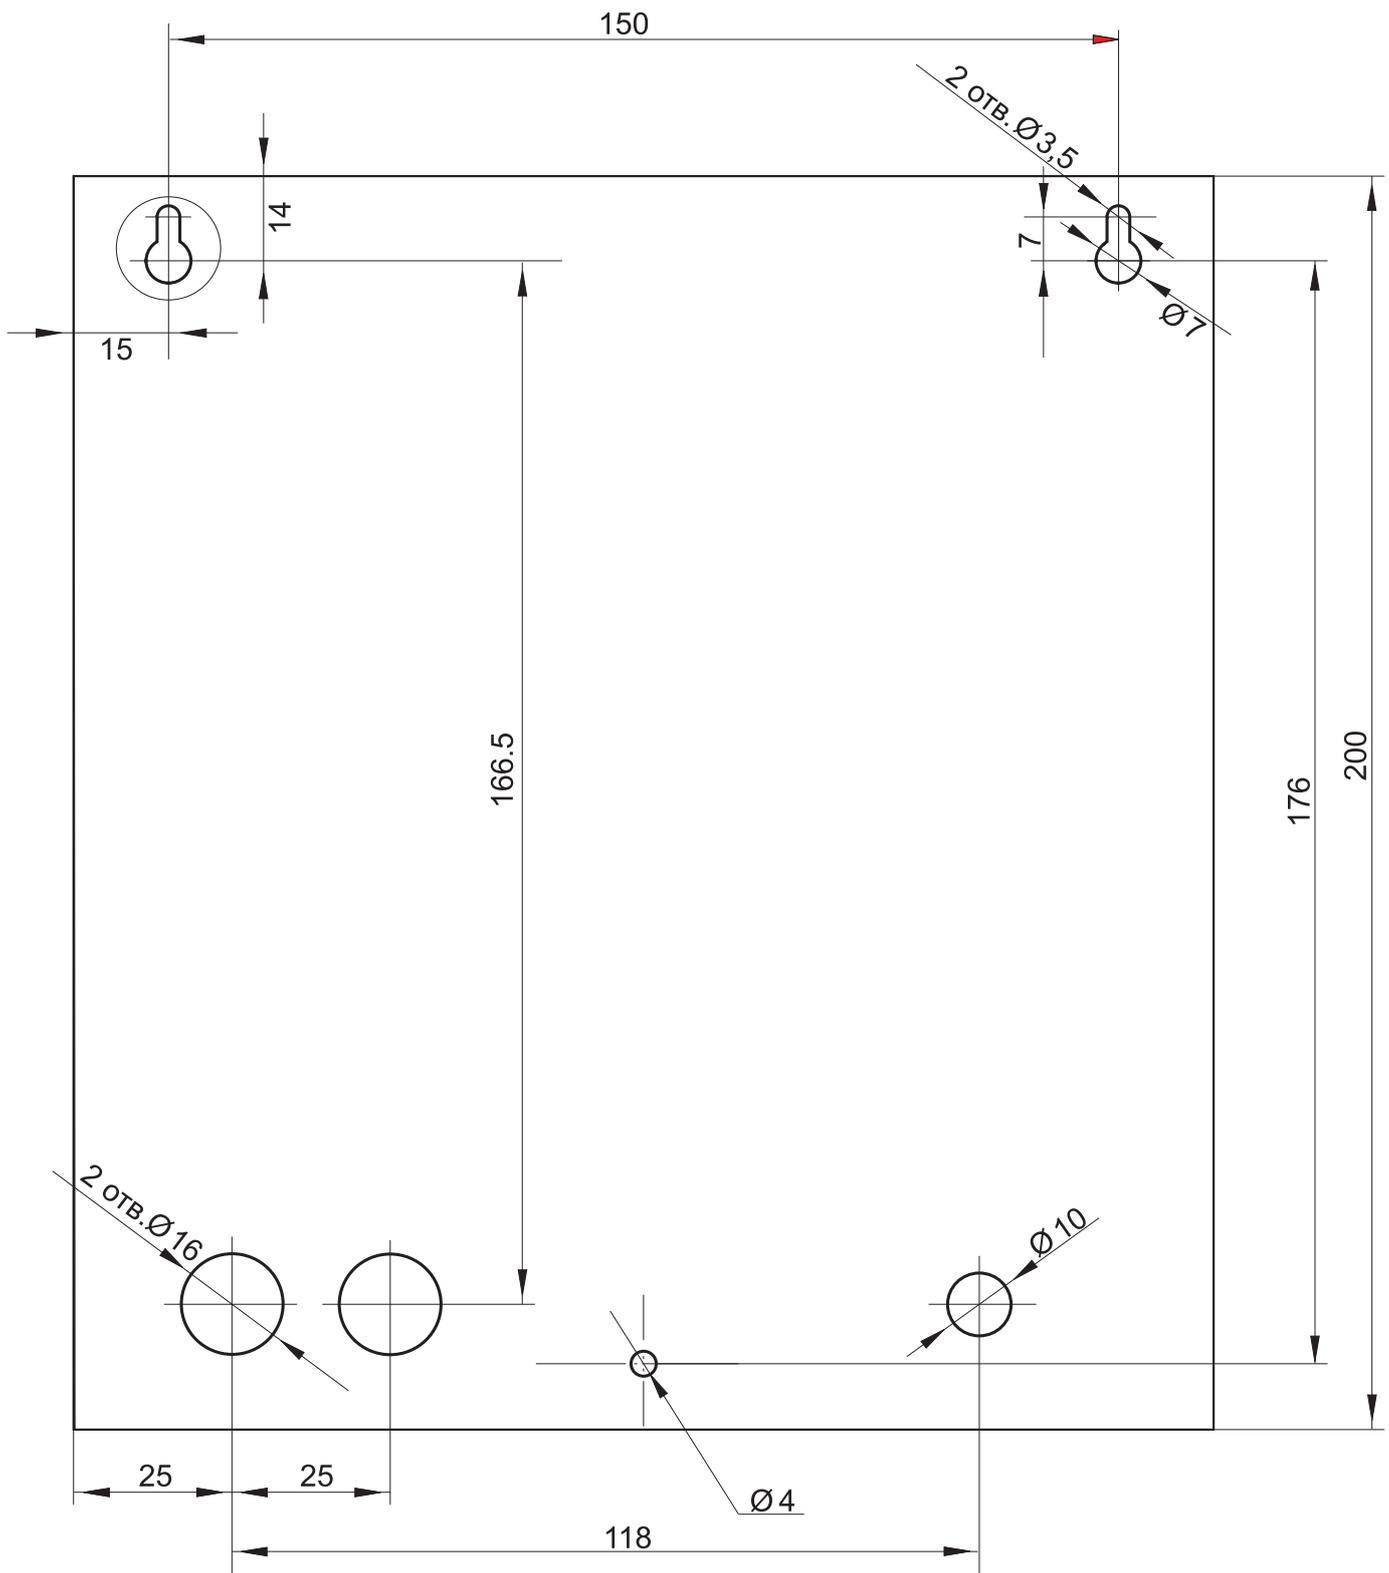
Разметка отверстий для крепления контроллера PERCo-SC-610T/L
